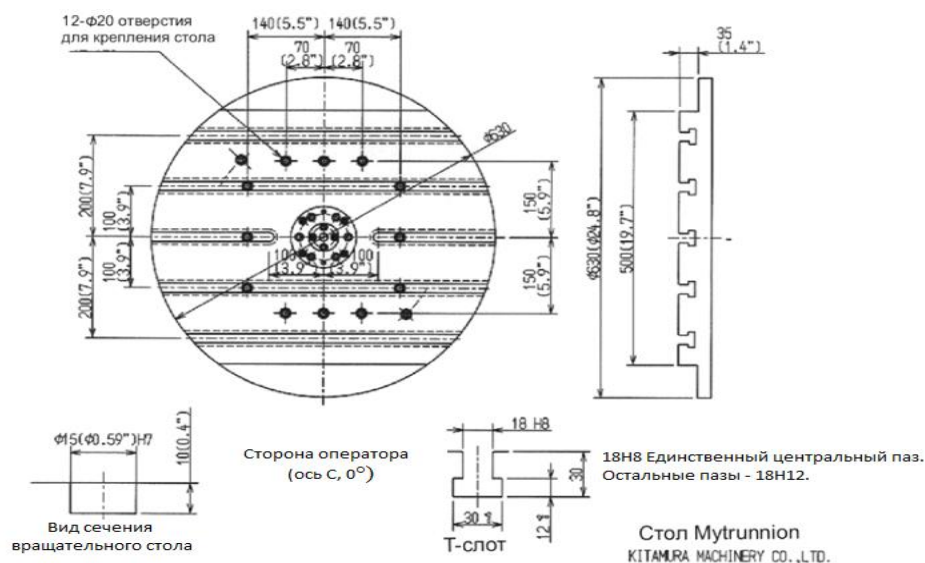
Приспособление для установки обрабатываемой детали
